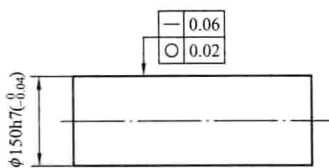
注有直径公差、素线直线度公差和圆度公差
